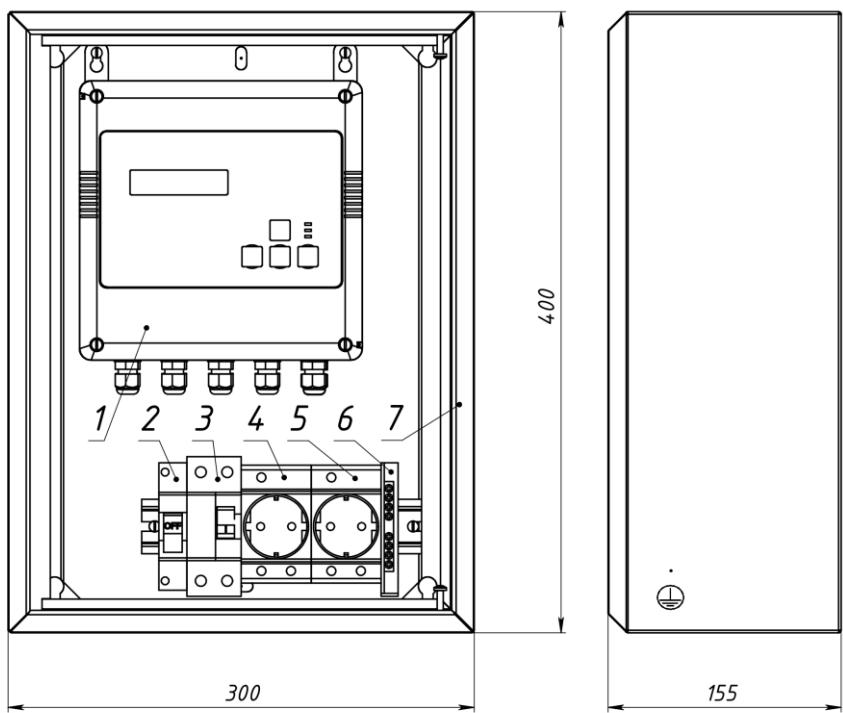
Габаритные размеры и основные компоненты шкафа управления установки ТЭСМАРТ-СТОК-01.
